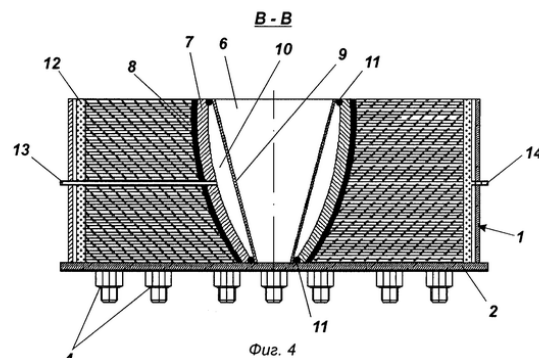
Взрывная камера патента 2619545 [3], сечение В-В: 1 - металлический наружный корпус в форме цилиндра, 2- дно цилиндра, 4- резьбовые соединения, 6 -рабочая полость, 7 - рабочая поверхность, 8 - компенсационная прокладка, 9 – заготовка; 10- вакуумная полость, 11 - уплотнительные, герметизирующие прокладки; 12 - гидравлическая камера;13 - вакуумная трубка, 14- патрубок
